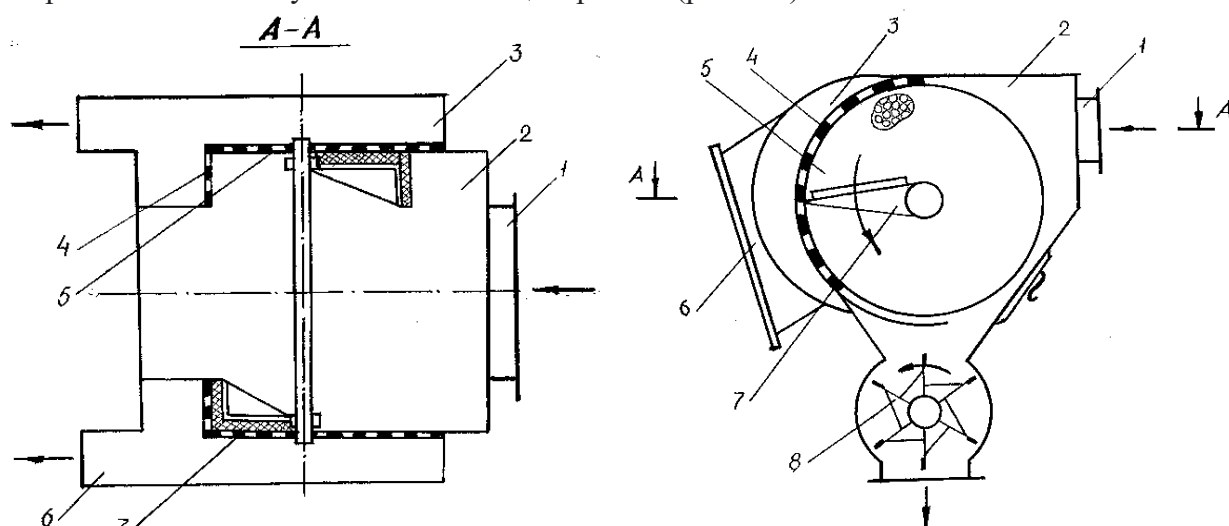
Дополнительный разделитель камер впускной патрубков-1, рабочая камера-2, дополнительная камера-3, дополнительная решетчатая поверхность-4, решетчатая поверхность-5, всасывающая труба-6, дренаж-7, вакуумный клапан-8.
